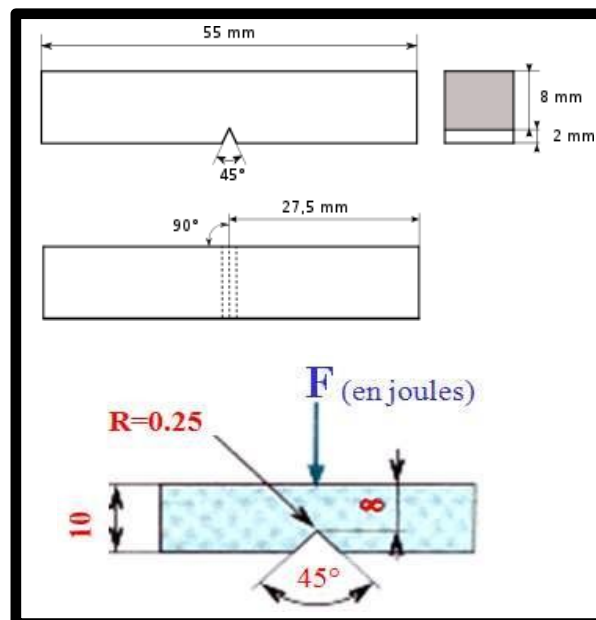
Dimensions et forme de l'éprouvette Charpy en V.
